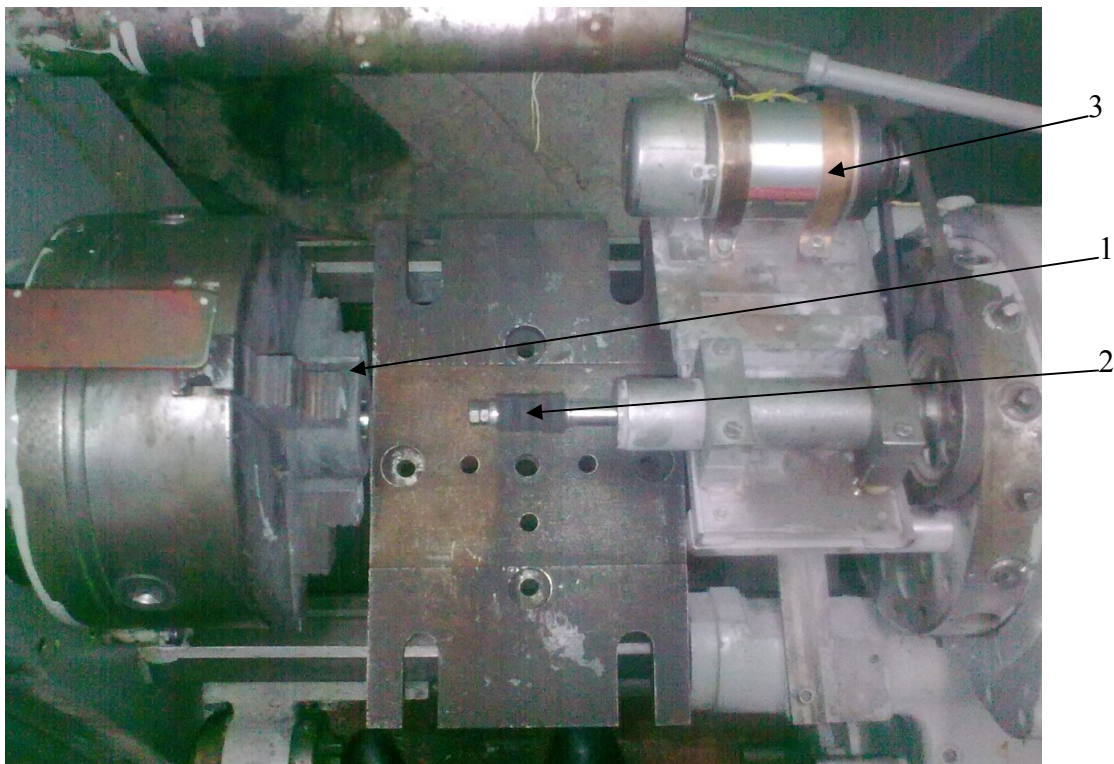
Вид сверху на экспериментальную установку для МАО внутренних поверхностей на базе токарно-револьверного станка 1341:
